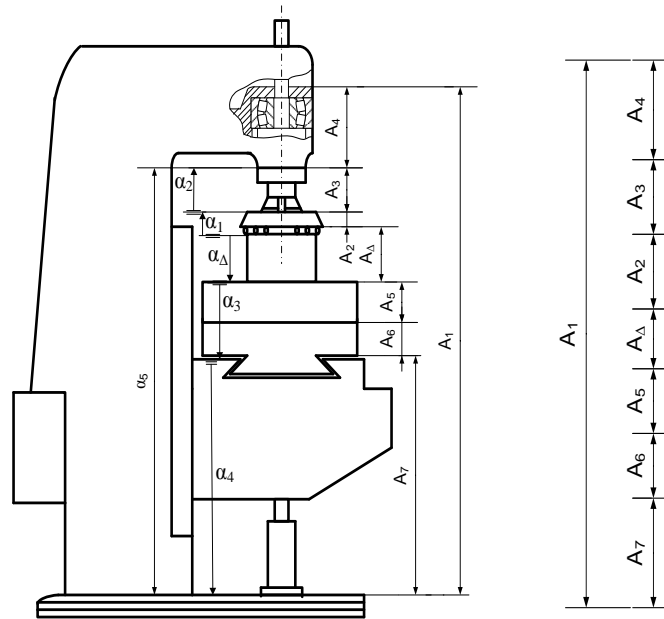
Розмірні ланцюги вертикально - фрезерного верстата
